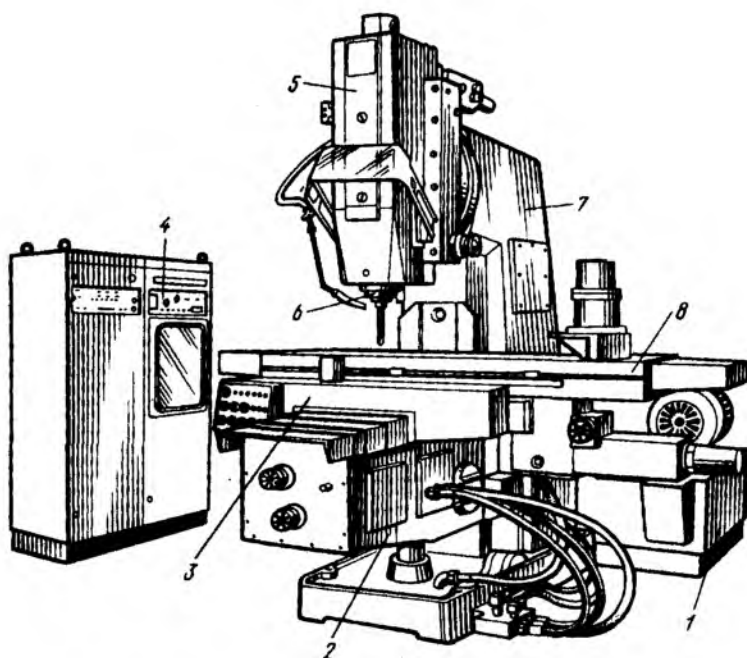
Общий вид фрезерного станка мод. 6P13Ф3
